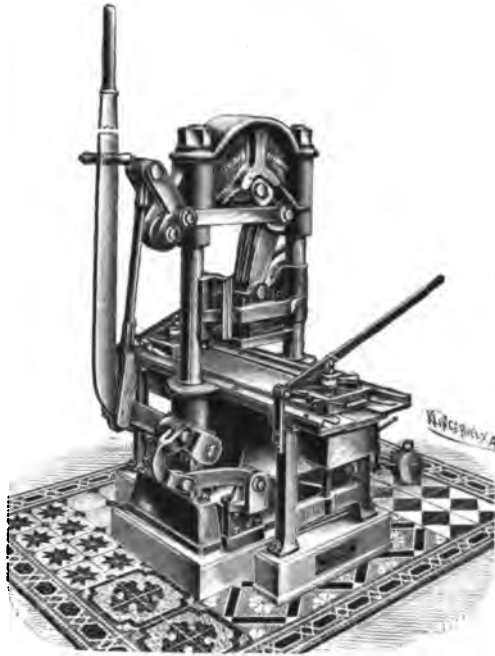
Kniehebelpresse, Bauart Bernhardt, mit langem, festliegendem Preßtisch für Handbetrieb.
